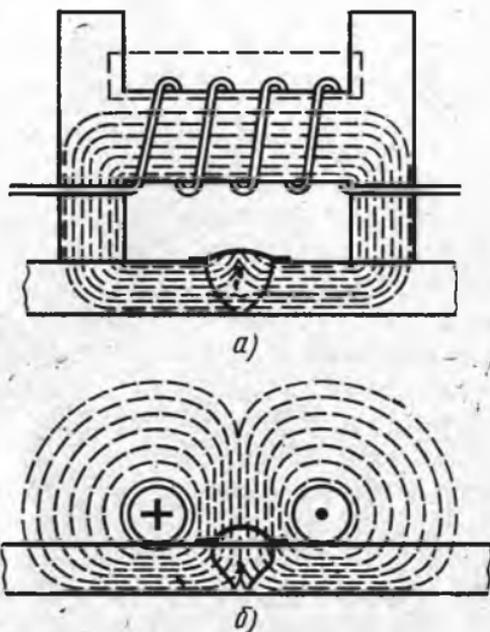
Намагничивание сварного шва с помощью:
